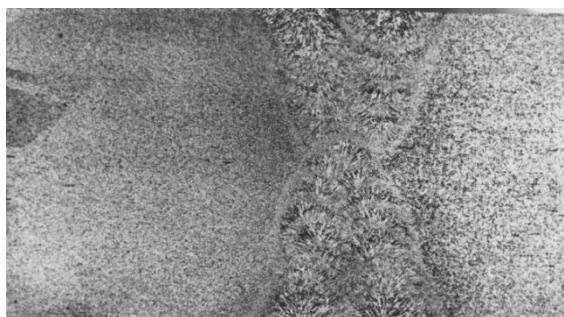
Макроструктура сварного соединения стали 09Г2С, выполненного АСФ, х 100
